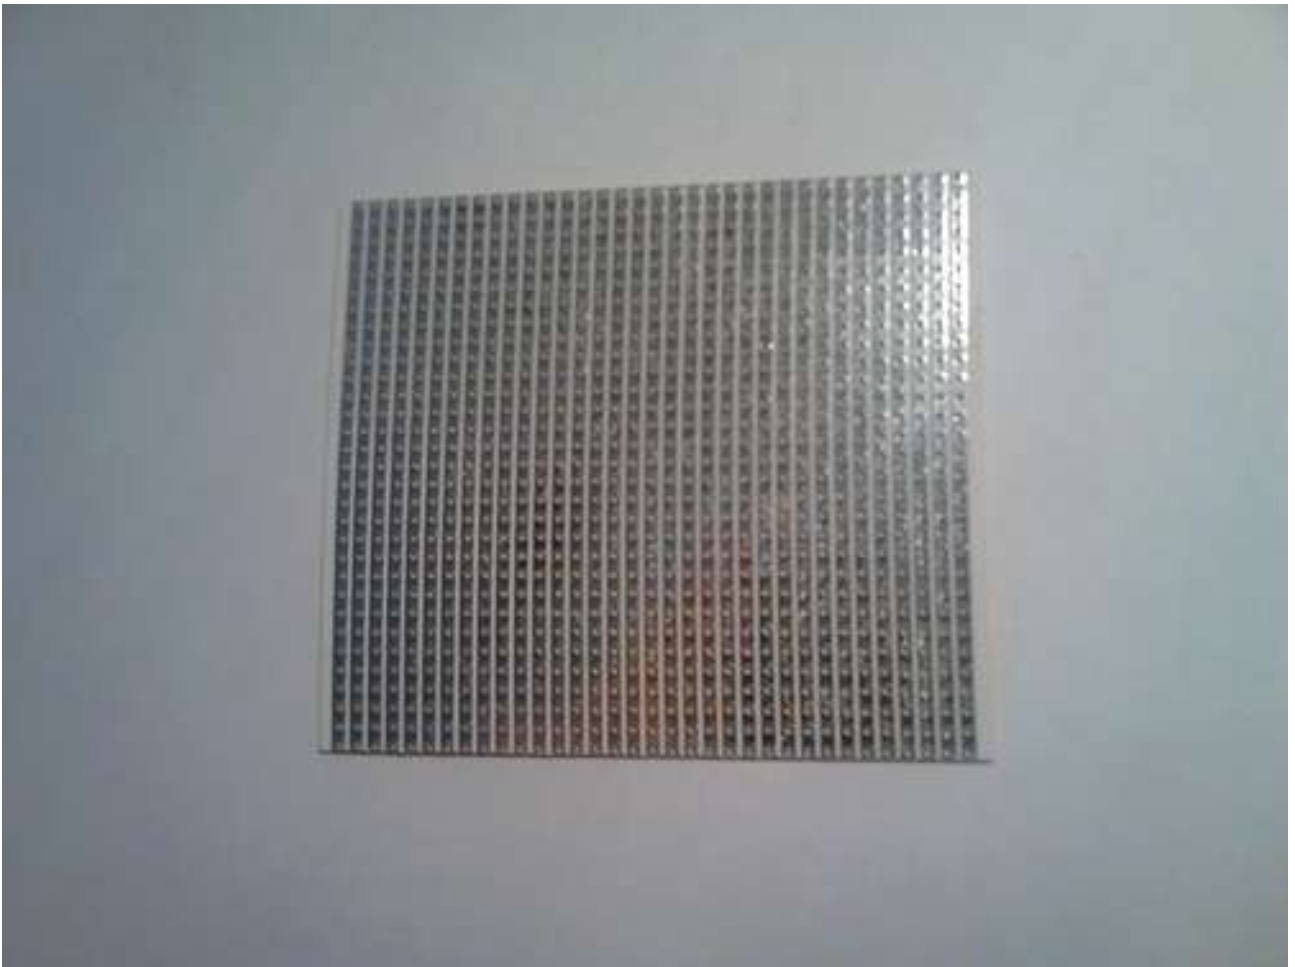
Placa de baquelita, cara de soldaduras
